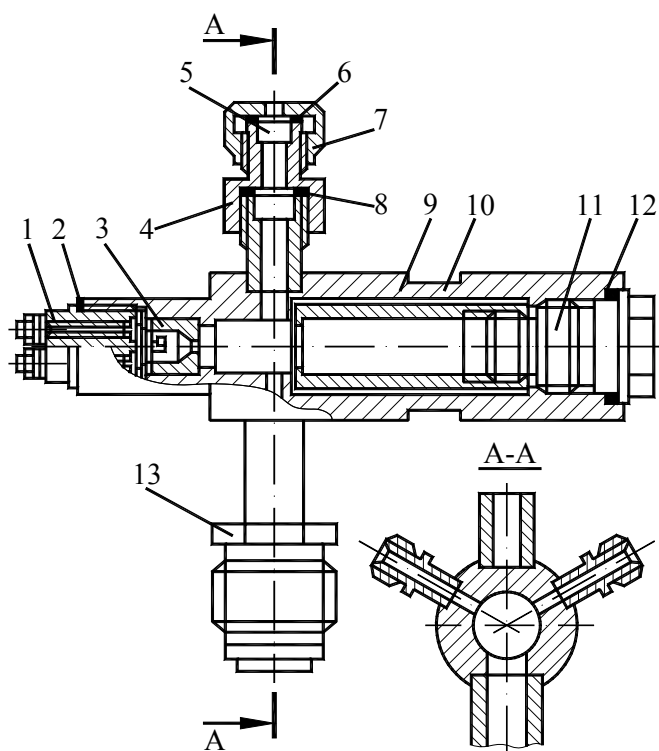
Схема камери згорання установки: 1 – вузол електроконтактів; 2 – прокладка; 3 – форсажна втулка; 4 – перехідник; 5 – вкладиш; 6 – запобіжна мембрана; 7 – гайка; 8 – прокладка; 9 – корпус камери; 10 – стакан з зразком ПНМС; 11 – заглушка; 12 – прокладка; 13 – гайка
